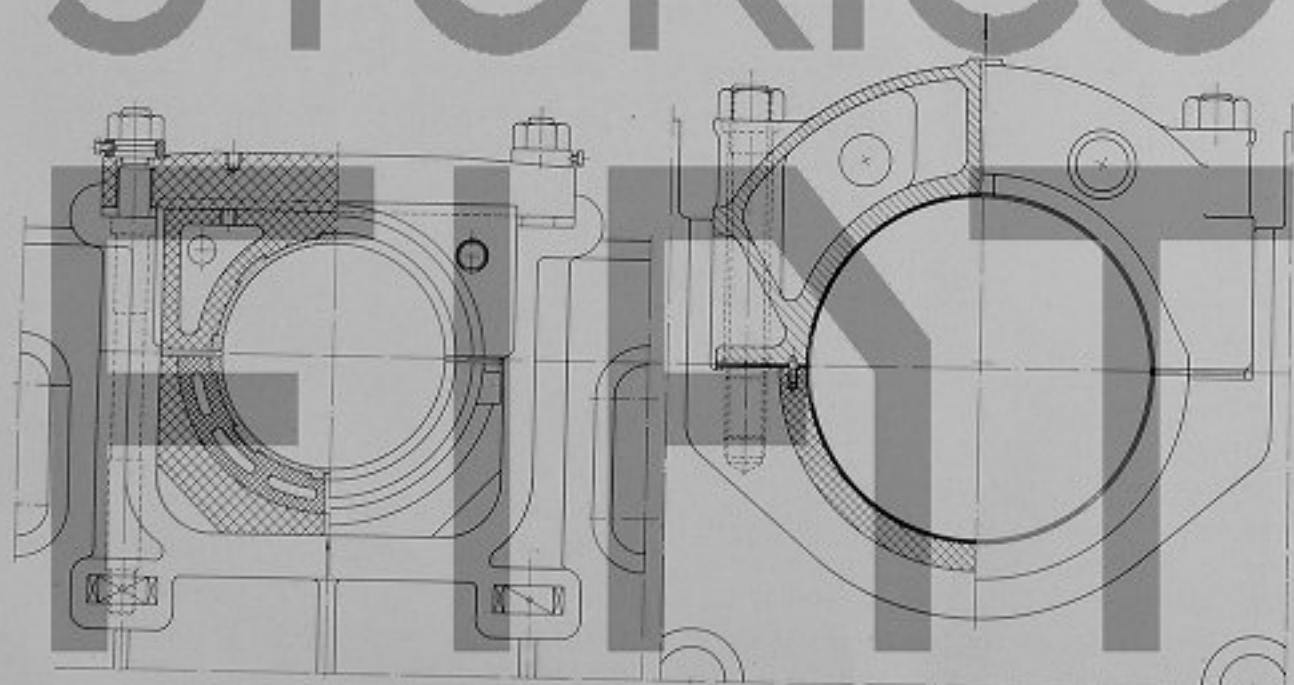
Confronto cuscinetti di banco motori 2C 176 e C 7605.
